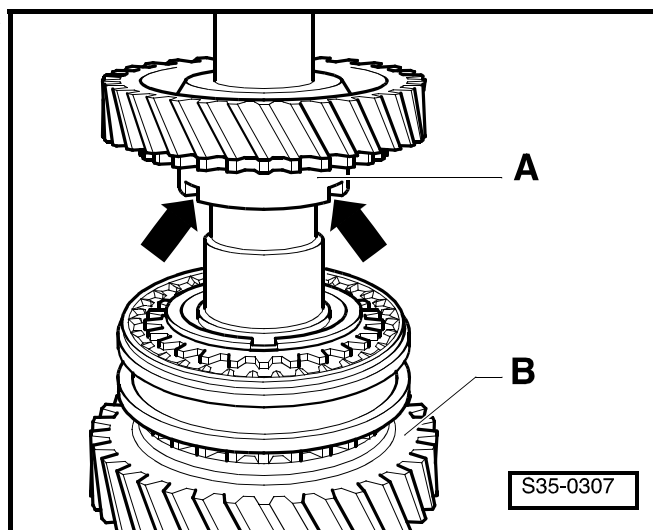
Положение для сборки скользящей муфты и каретки синхронизатора 3-ей и 4-ой передач
